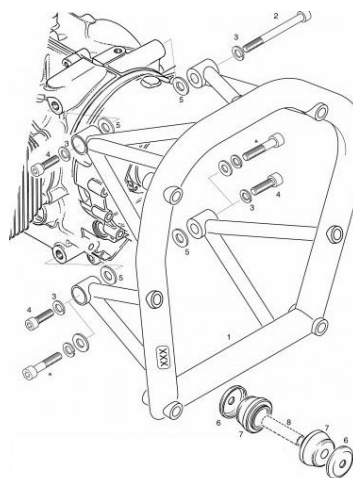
Castello motore per Rotax 912; (b) Suspension frame per Rotax 912.
